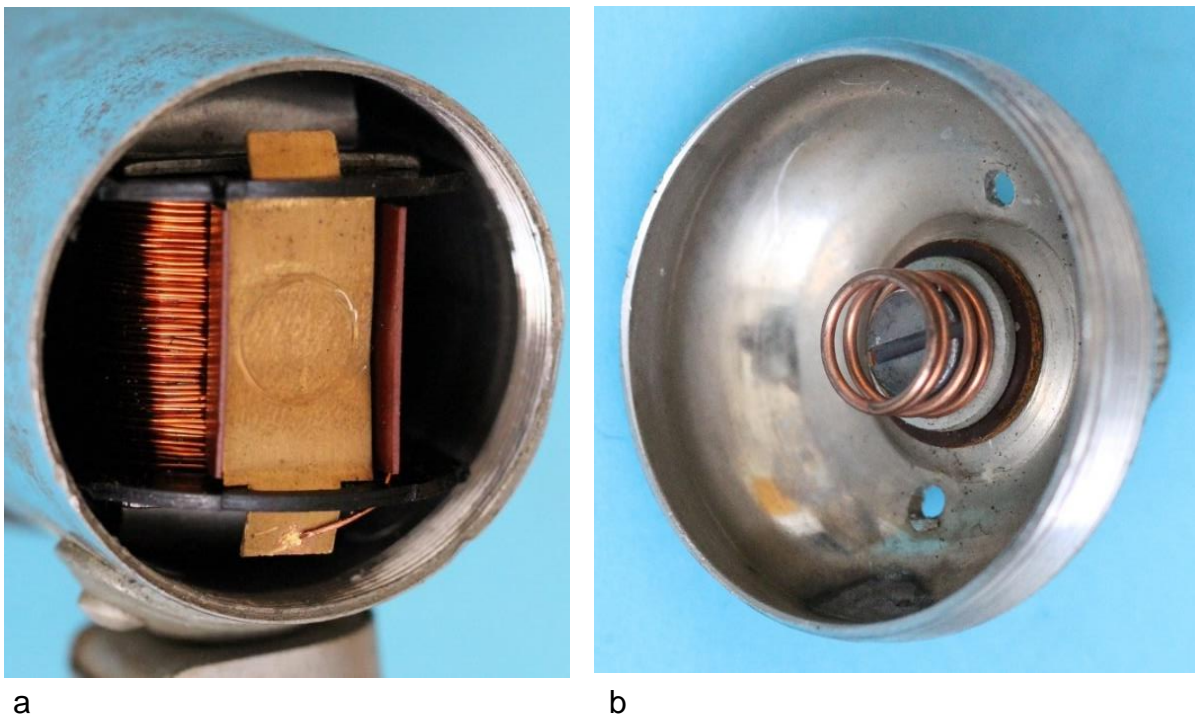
Boden mit Montagebohrungen: a) Spannung führendes Kontaktblech, b) Feder für die Kontaktierung mit dem Kontaktblech
